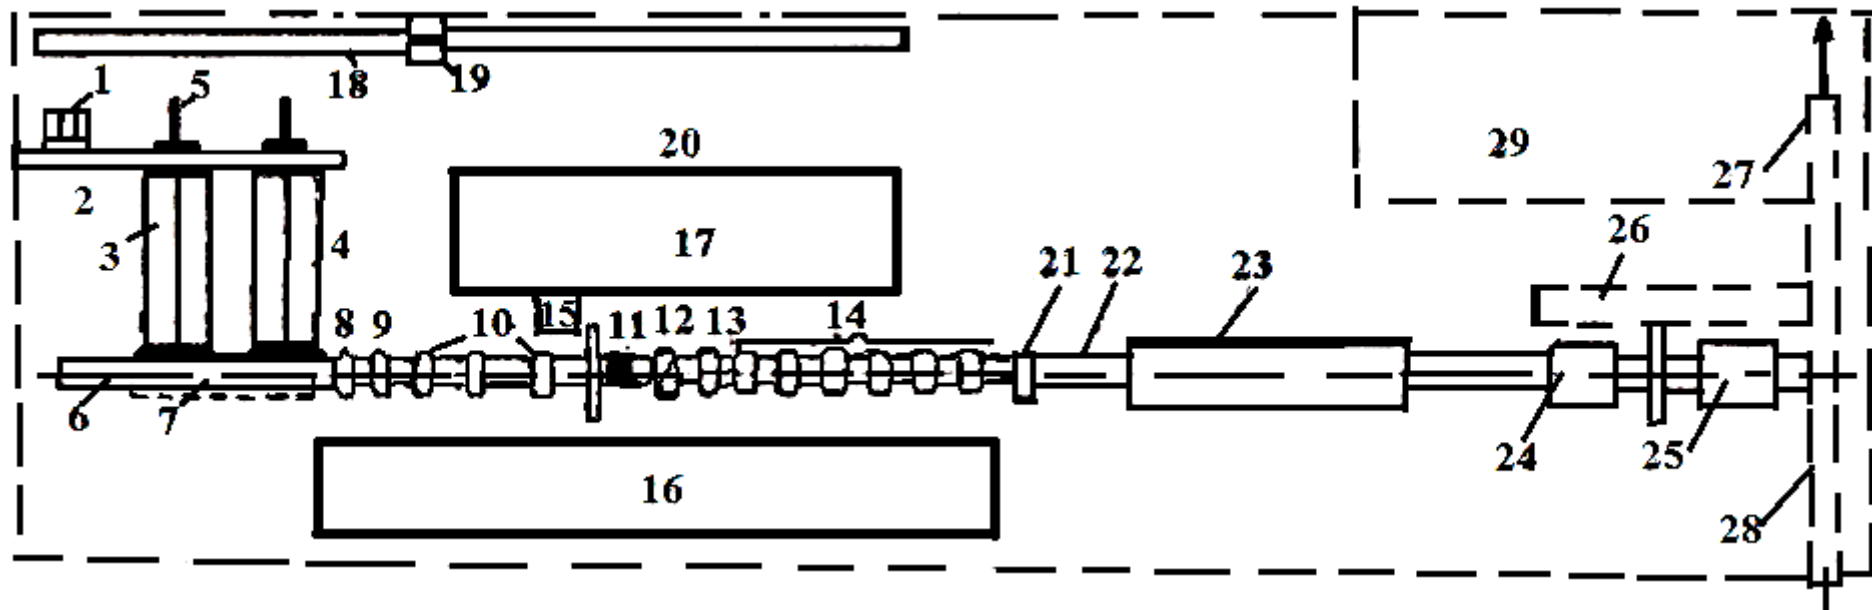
Схема розташування обладнання ШСГП 1680:
